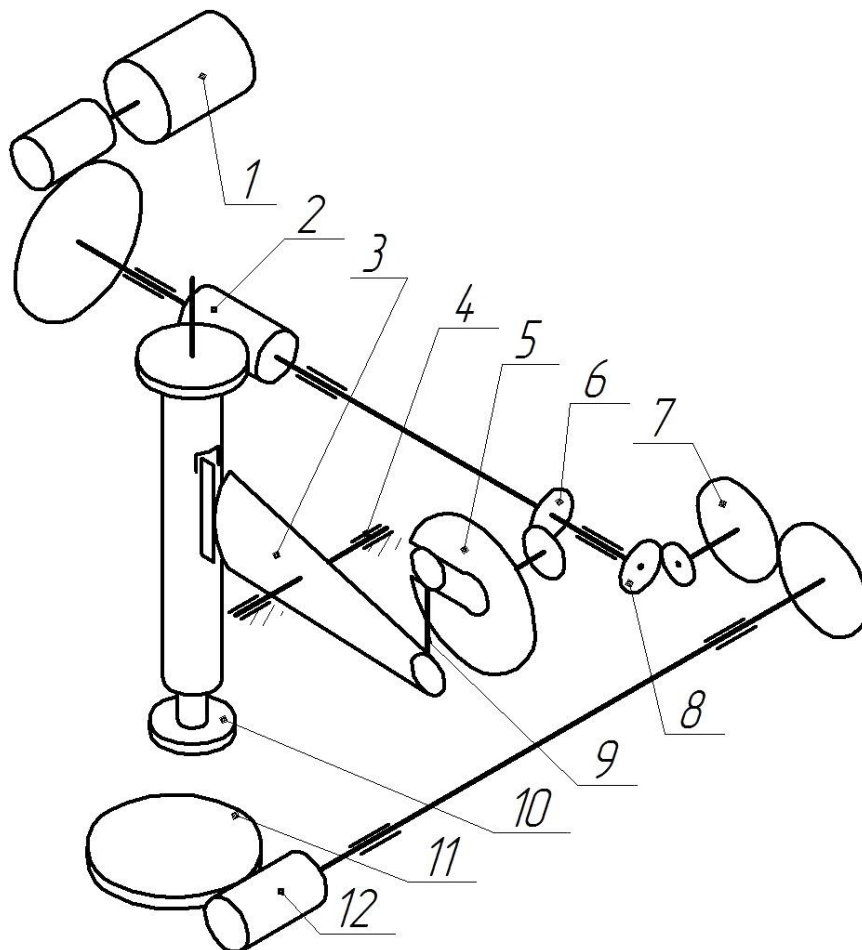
Кинематическая схема зубодолбежного станка в аксонометрической проекции
